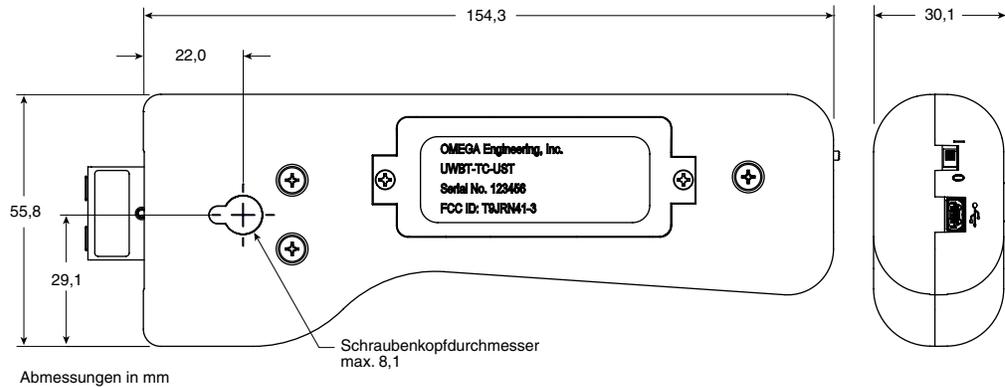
Abmessungen des UWBT-Messumformers
